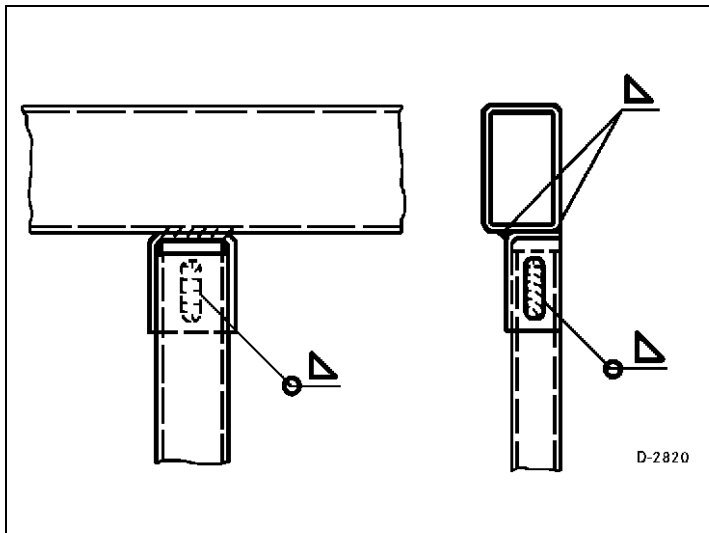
Soldar soportes, refuerzos para el piso, etc.
